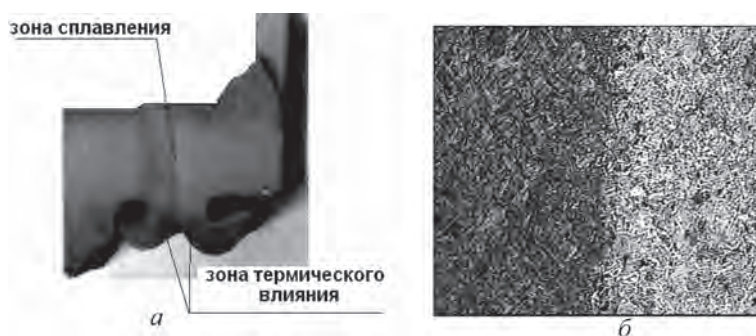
Сварной шов при сварке трением: а – внешний вид шлифа; б – микроструктура зоны сплавления. ×125
